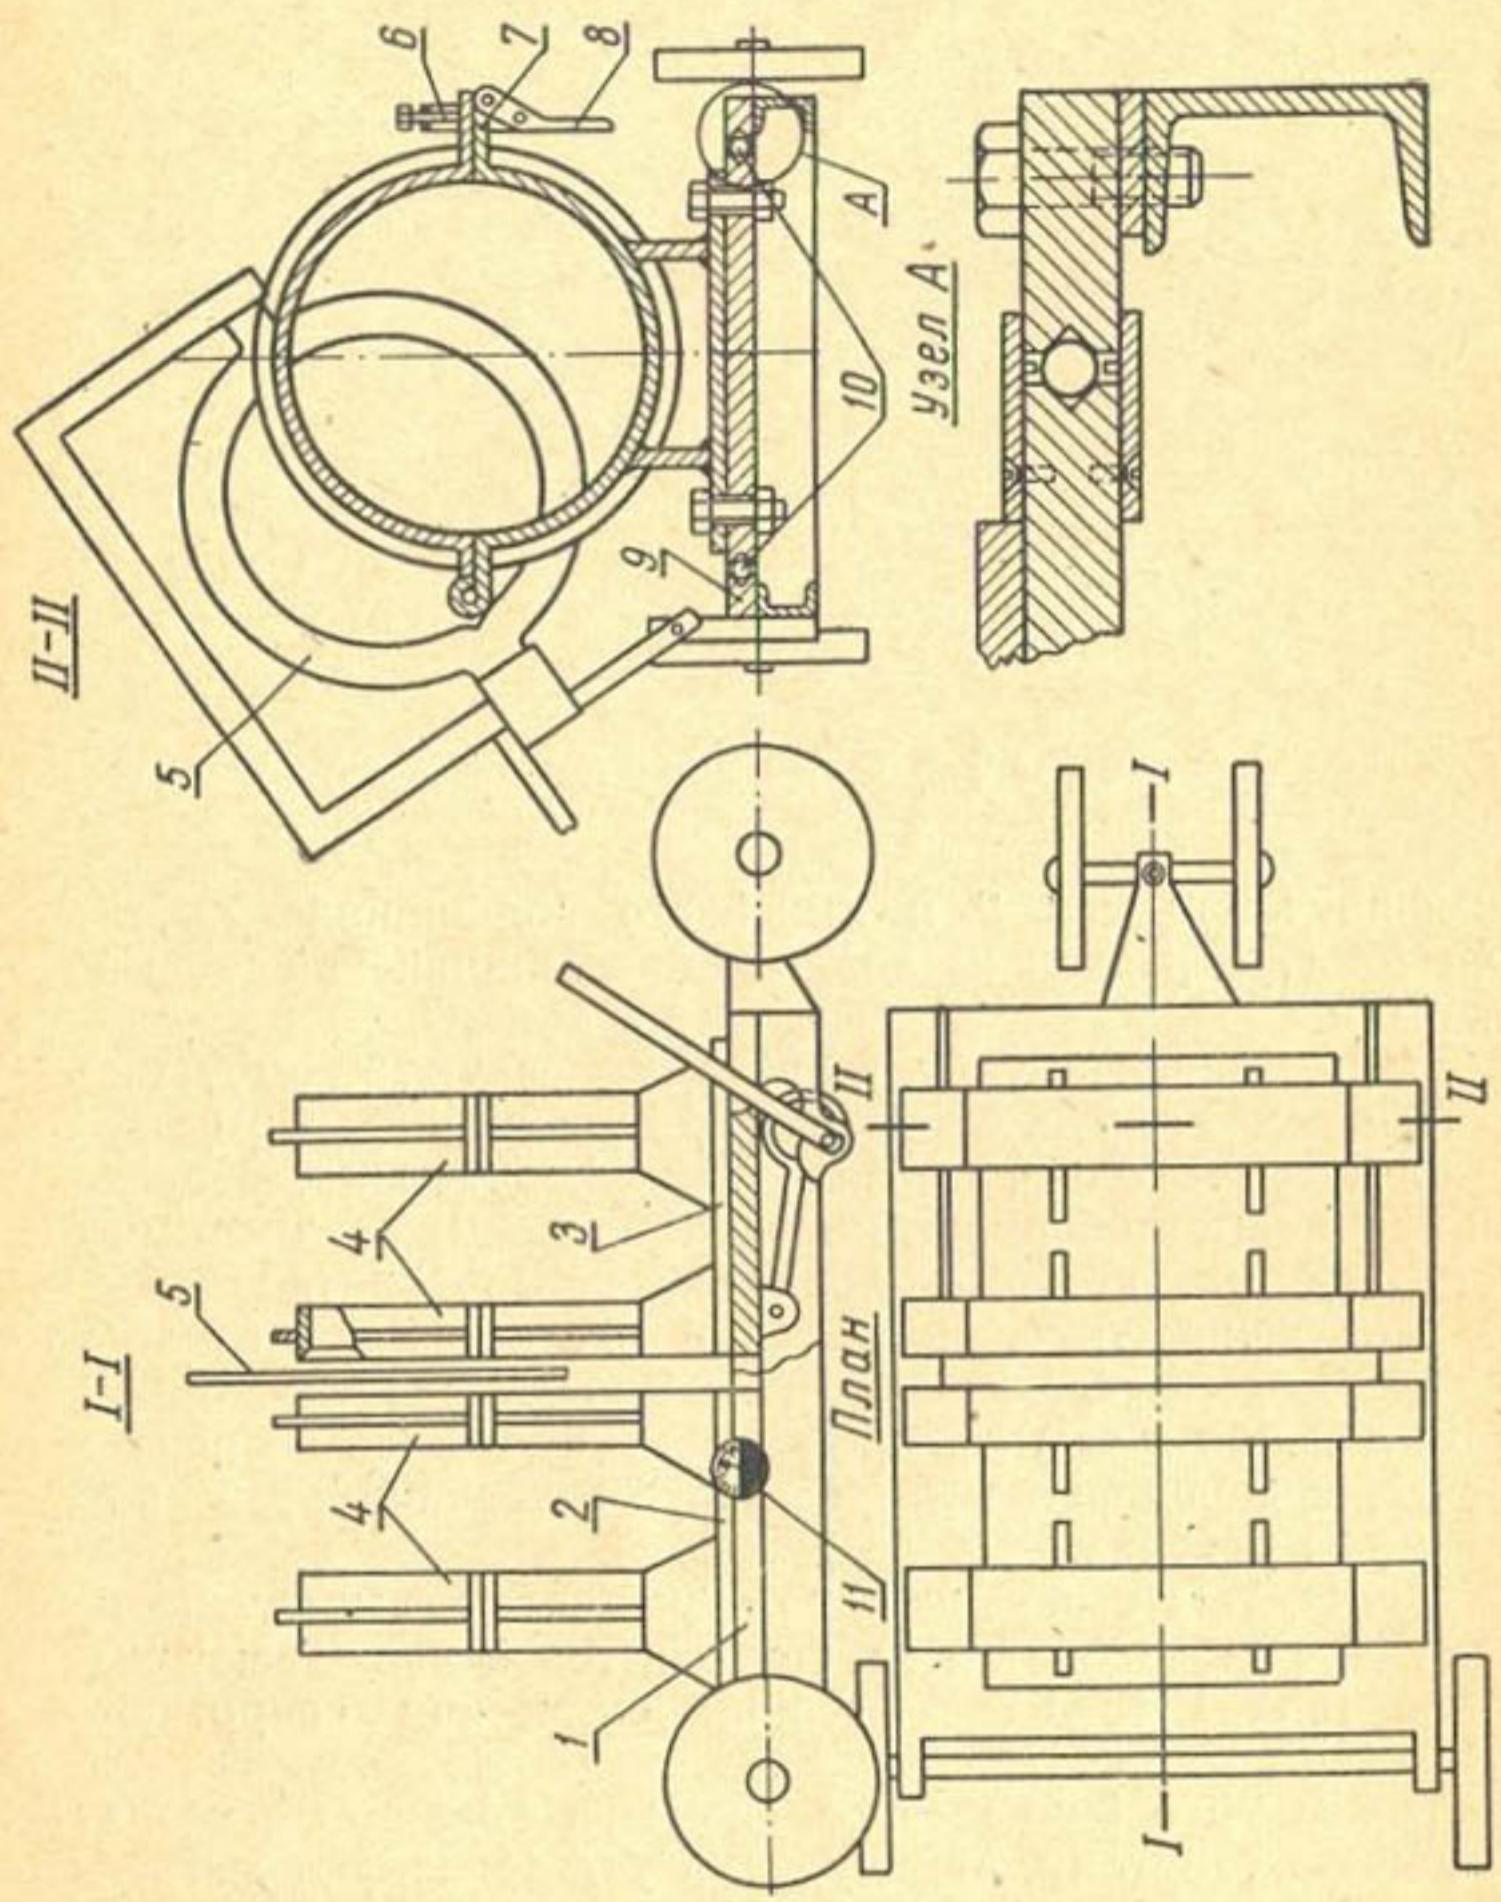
Схема установки для сварки полиэтиленовых труб встык:
